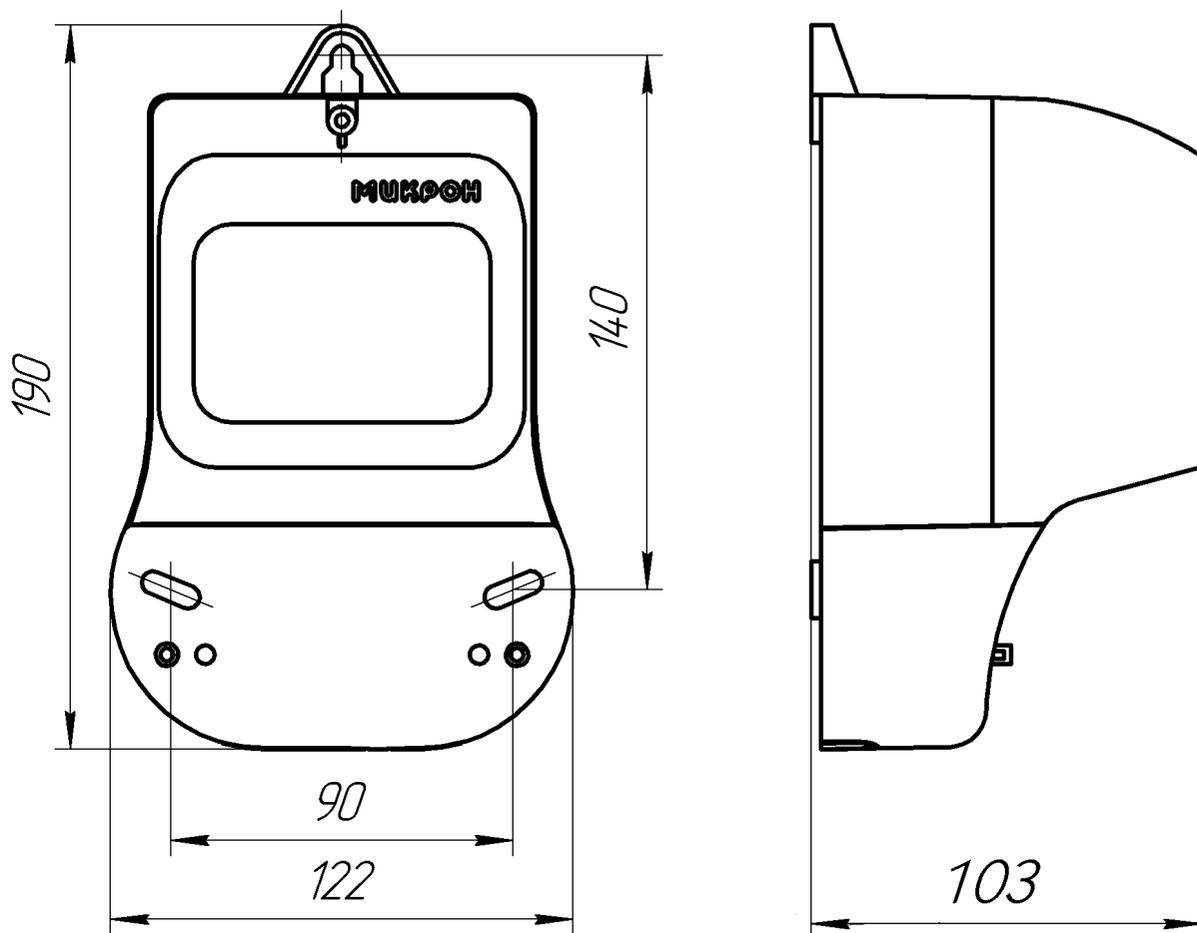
Габаритный чертеж и установочные размеры счетчиков
